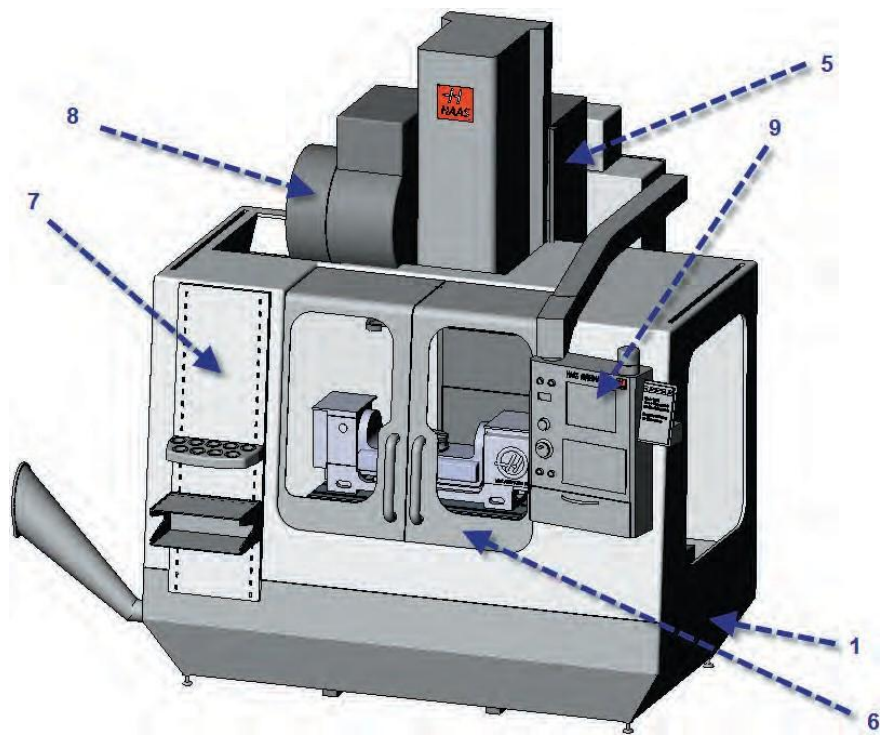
Корпус вертикально-фрезерного верстата зі ЧПК
